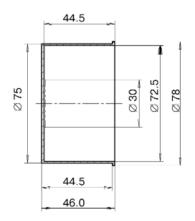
Стакан металлический для поверки поверхностных зондов Материал - сталь нержавеющая 12X18H10T
